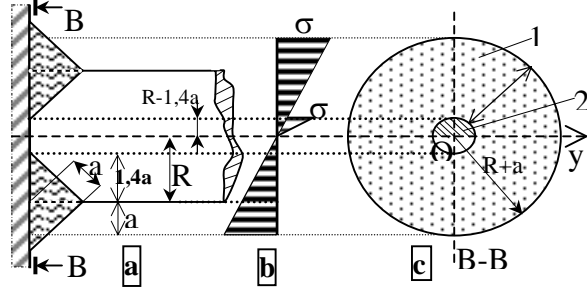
Schematisierung der Schweißnaht und der mechanischen Spannungen
